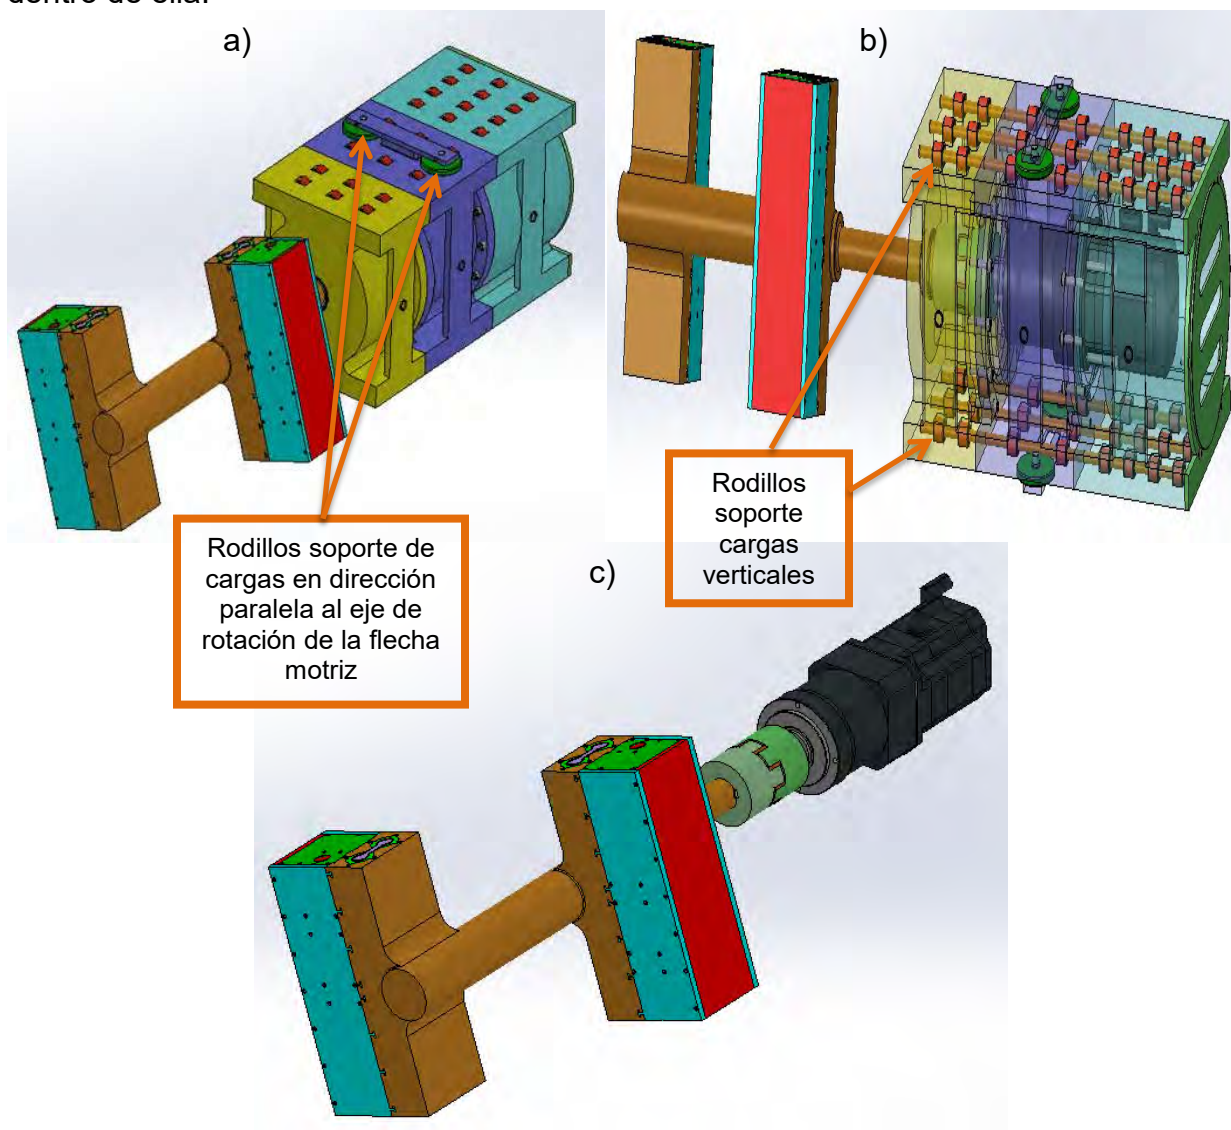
Configuración final del conjunto motor, a) Vista en 3D, b) Vista de los componentes internos, c) Detalle de los componentes internos
